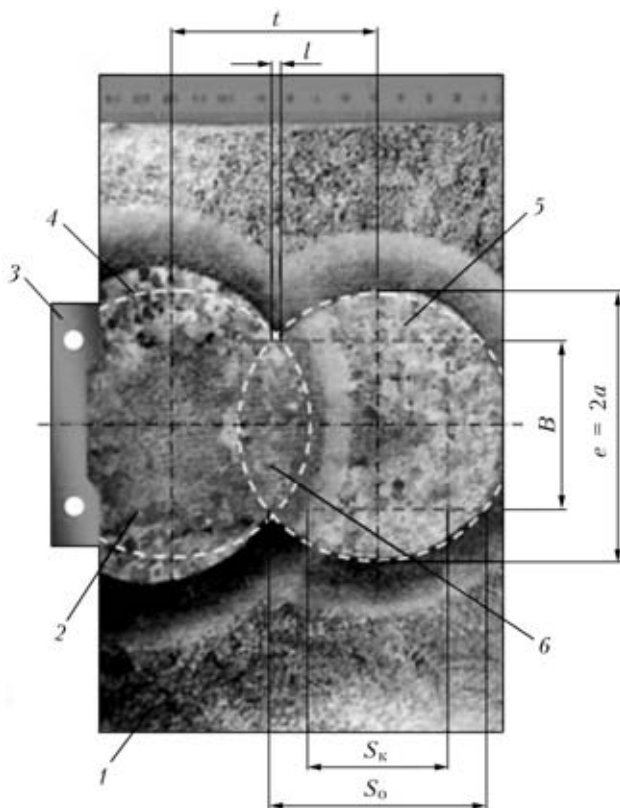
Поперечный макрошлиф фрагмента многослойного электрошлакового шва: 1 — свариваемые детали образца; 2 — форма разделки кромок под МЭШС; 3 — формирующее водоохлаждаемое устройство; 4 — расчетная форма линии (зоны) сплавления; 5 — слой шва; 6 — формирующая пластина-проставка
